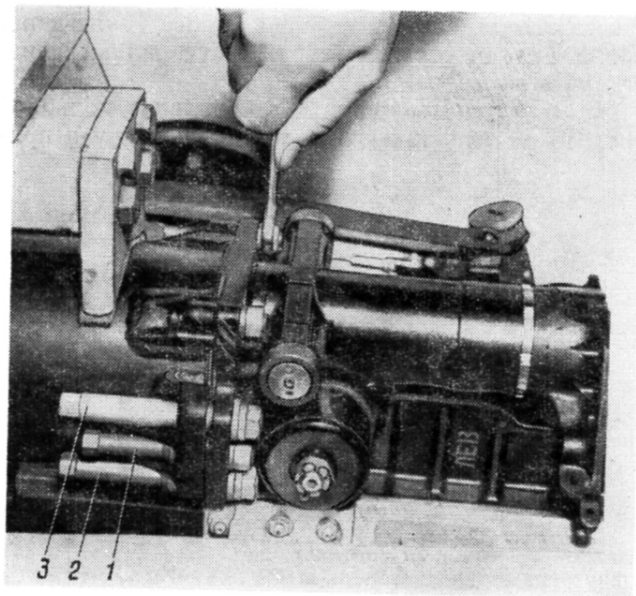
Ослабление гаек крепления болтов соплового блока:
